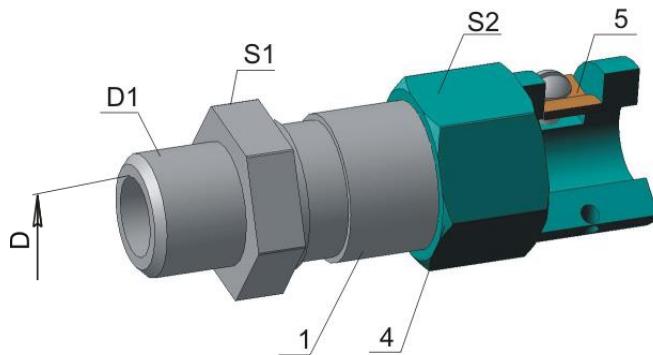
Конструкция кабельного ввода для монтажа кабеля
